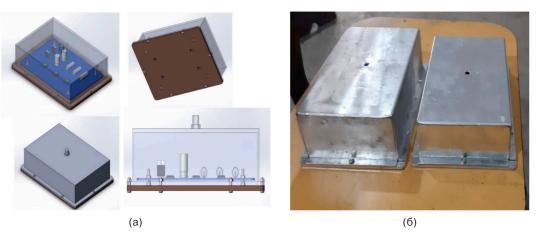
Вид модели блока БРЭСКА (а) и реального образца (б)
